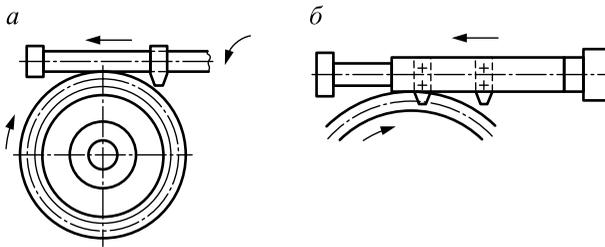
Схемы зубонарезания червячных зубчатых колес резцами
